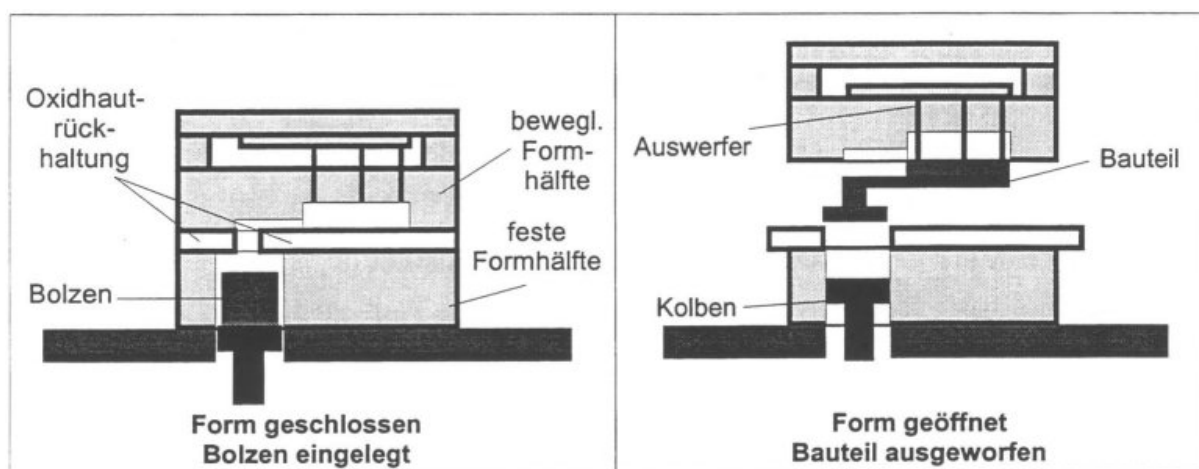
Werkzeugkonzept der Fa. EFU zum Thixogießen von Stahl [HIR-99]
